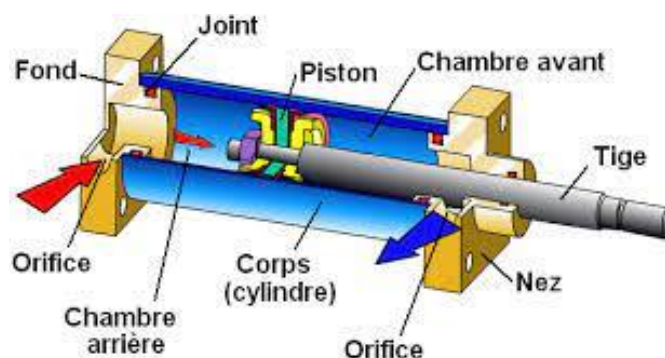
Vue en coupe d'un vérin pneumatique
